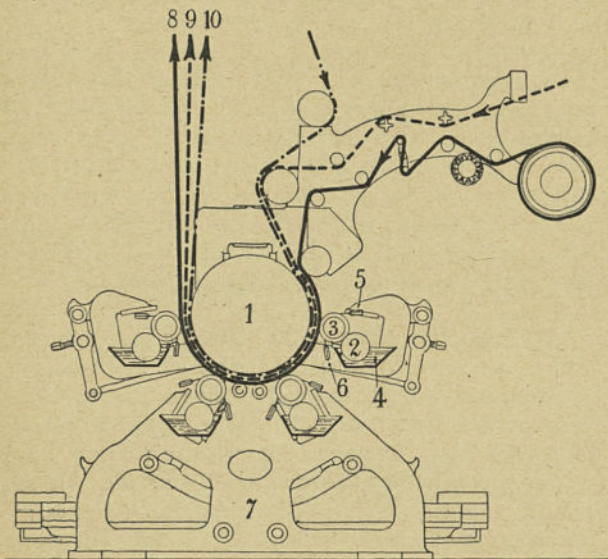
MACHINE A IMPRIMER 4 COULEURS.
